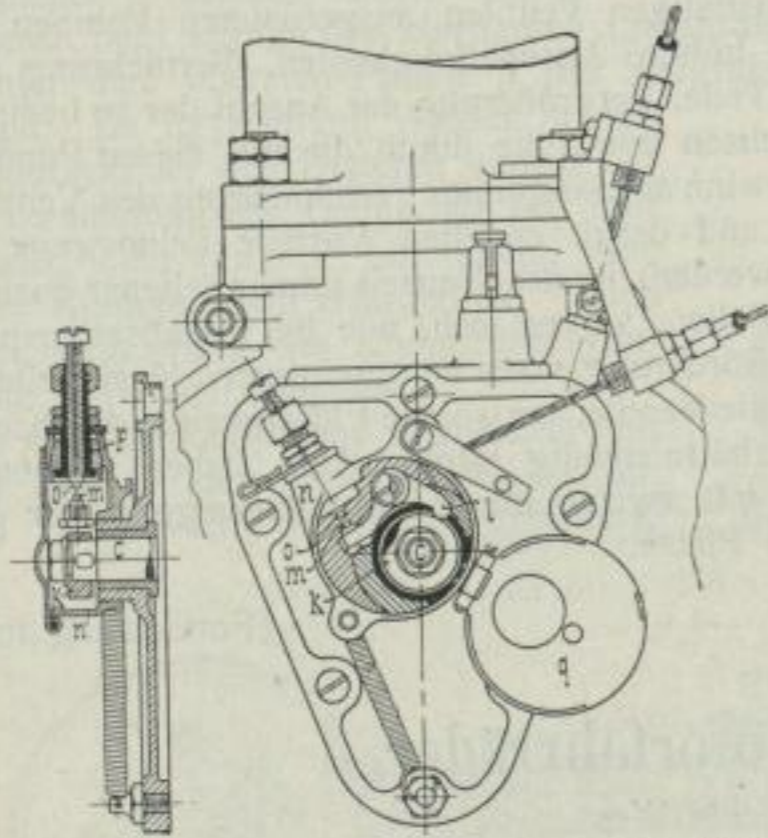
Steuerung für die Zündung beim Adler-Motor.
